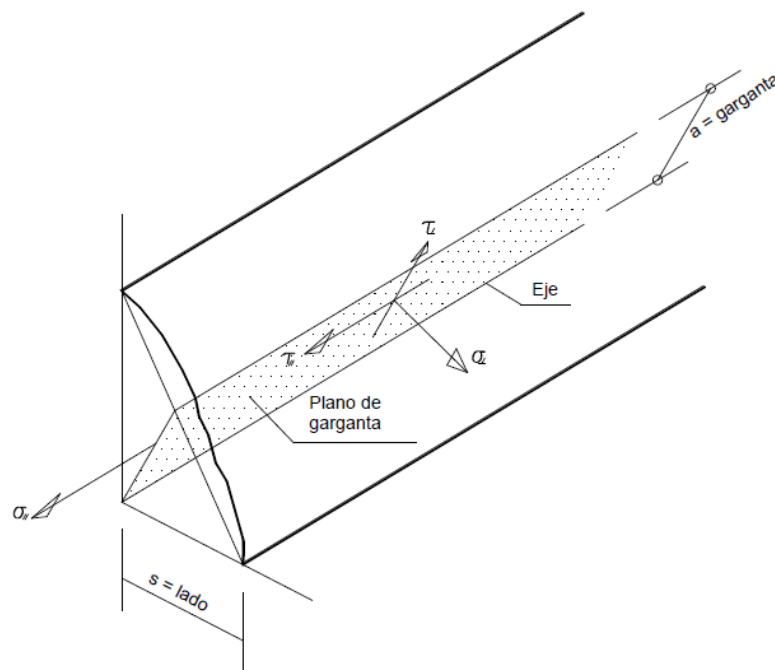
Partes de la soldadura (fuente EAE)
